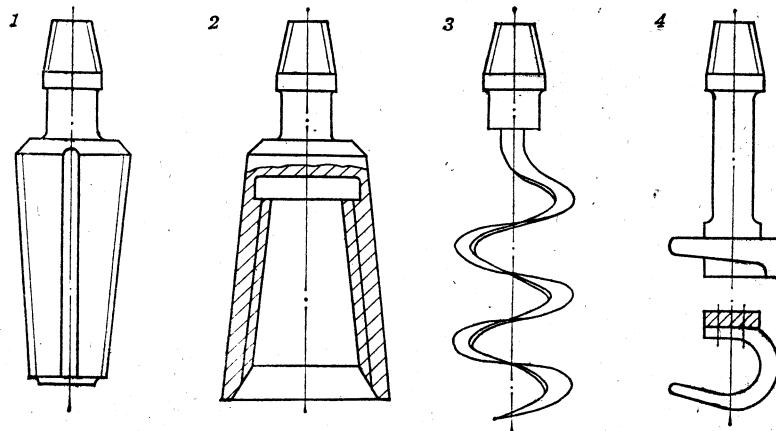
Ловильный инструмент: 1 — винт (метчик); 2 — колокол; 3 — штопор; 4 — «счастливый» крюк
